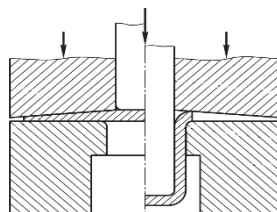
Схема вытяжки цилиндрической детали из переменной по толщине заготовки [3, 14]
